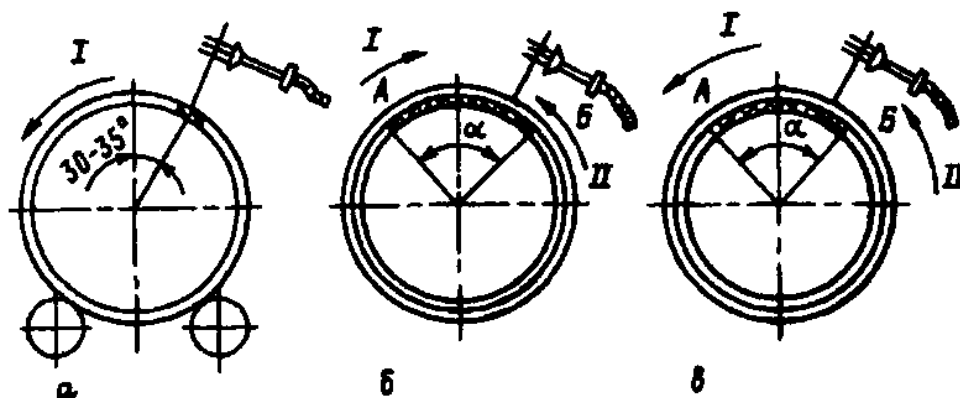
Порядок сварки стыка труб с поворотом на 360° :
